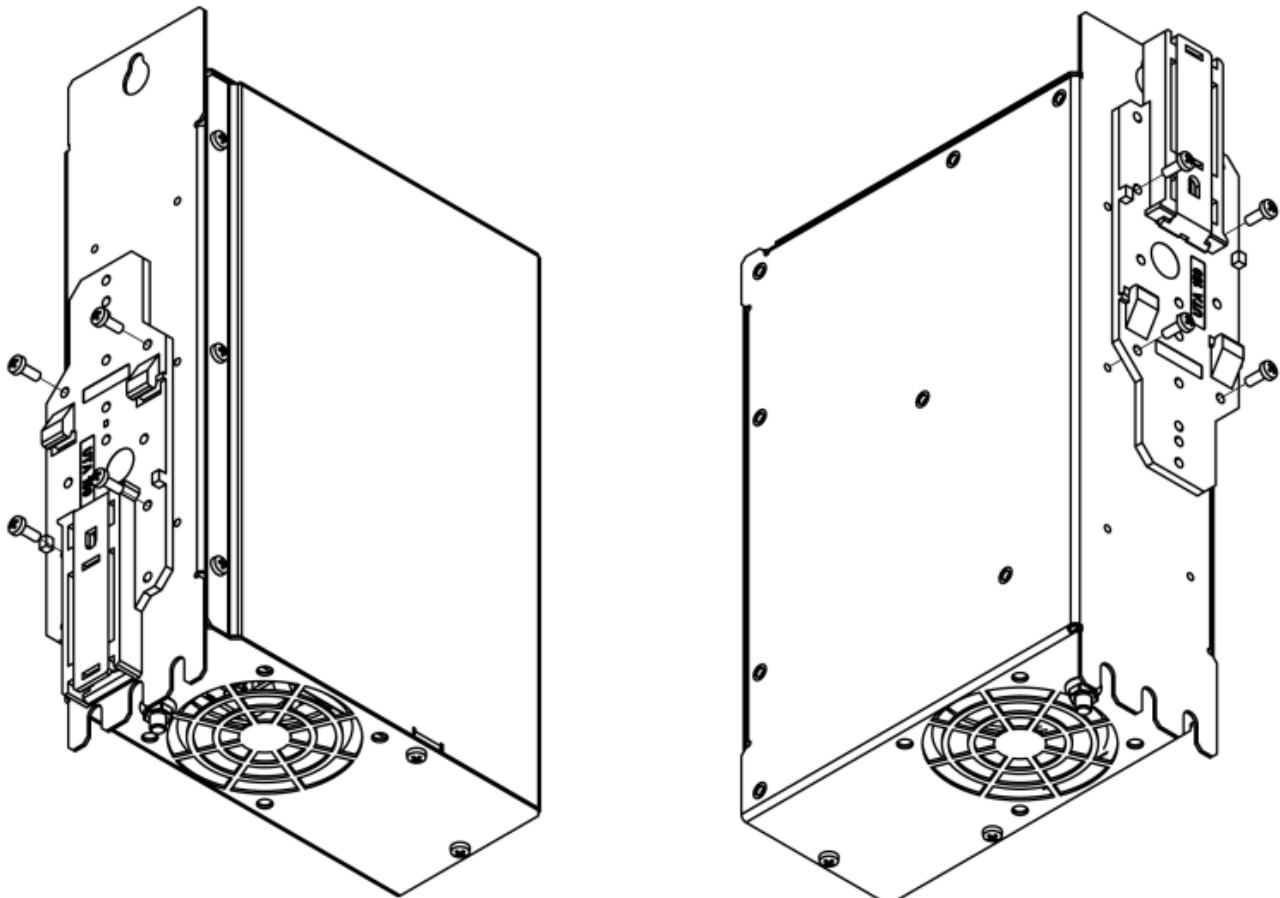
Montaggio su guida DIN inferiore a sinistra, montaggio su guida DIN superiore a destra
